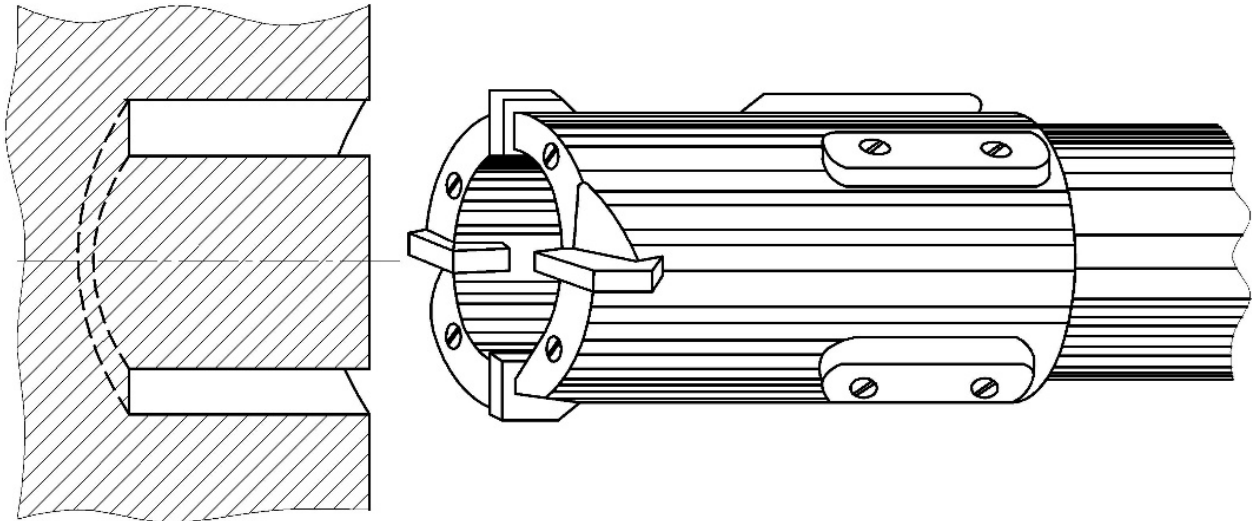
Схема оброблення свердлом для кільцевого свердління
